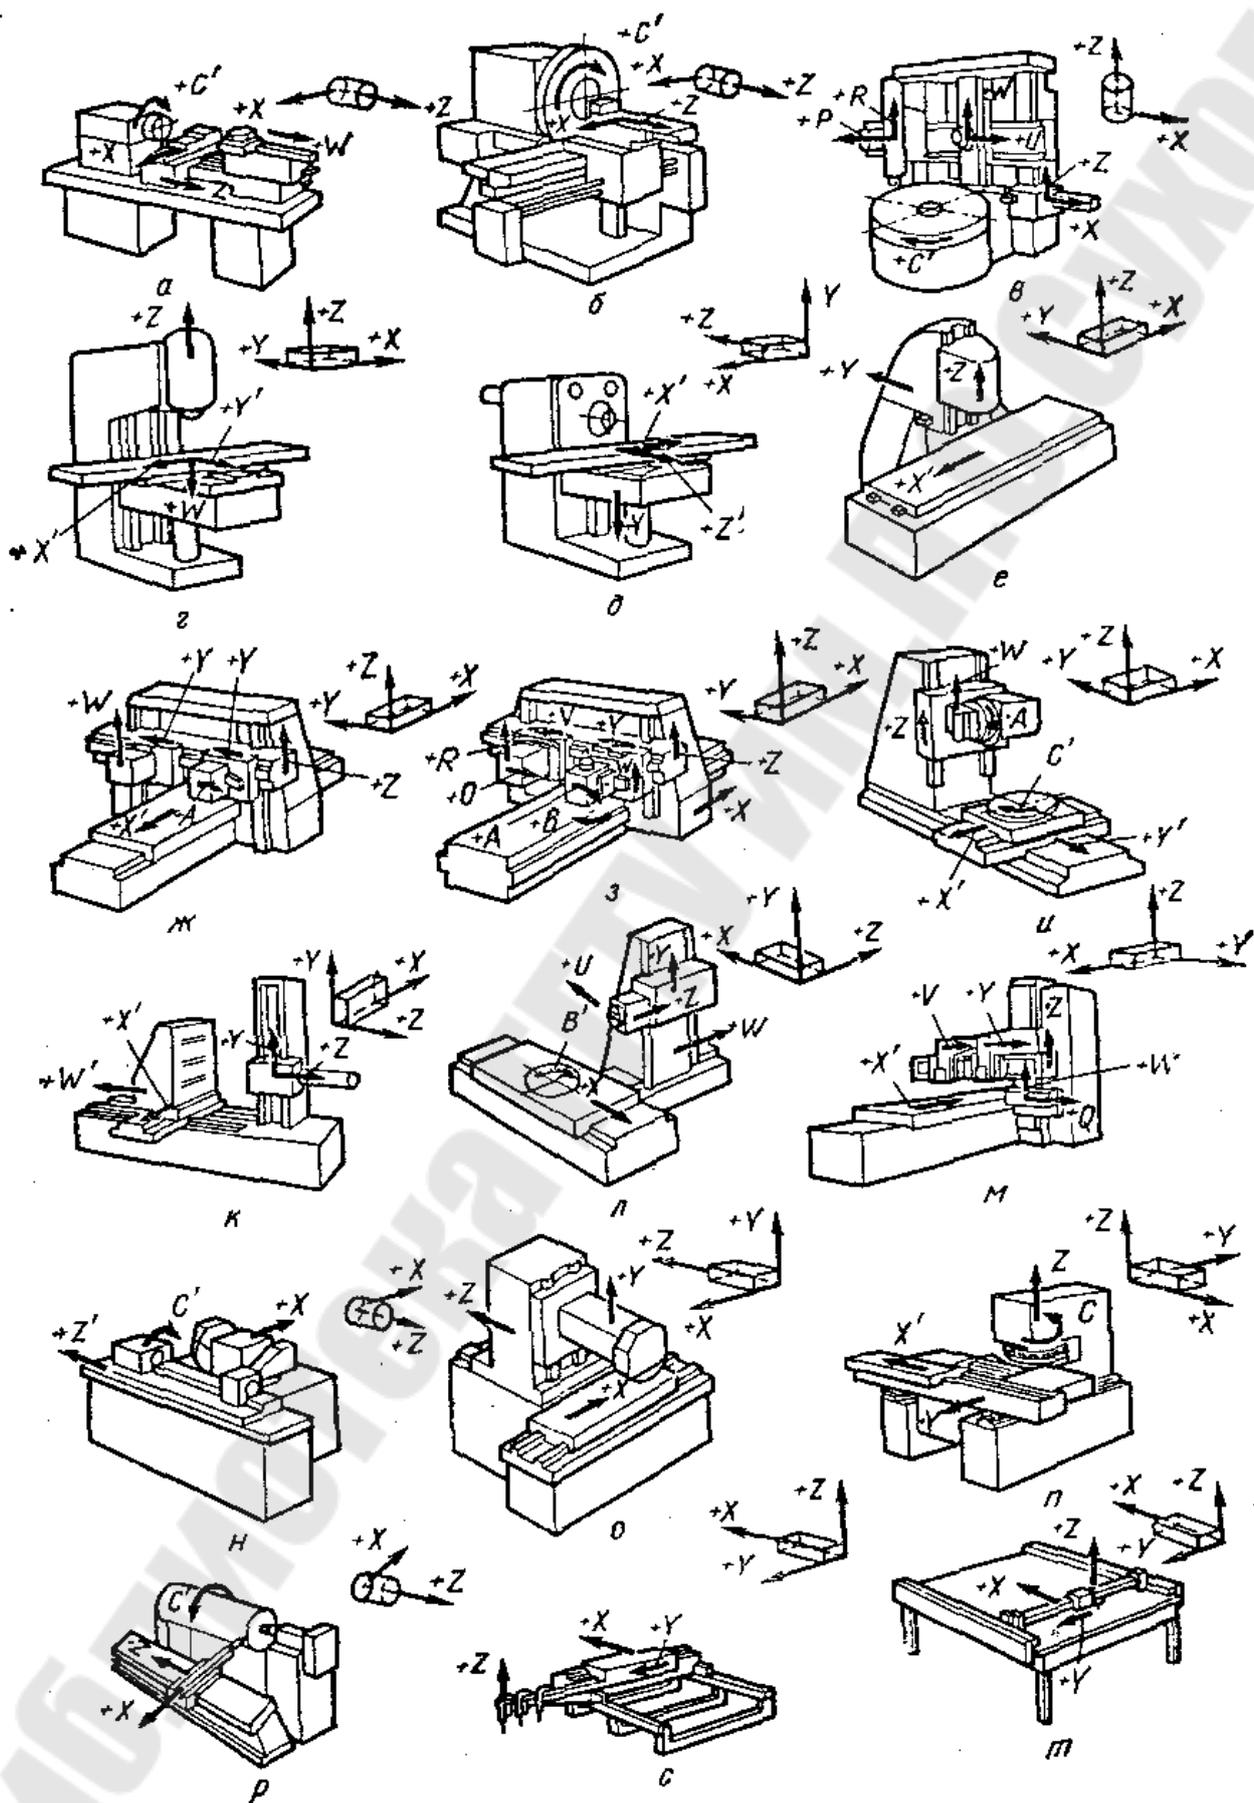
Компоновки металлорежущих станков с ЧПУ и расположение осей координат в станках с ЧПУ
